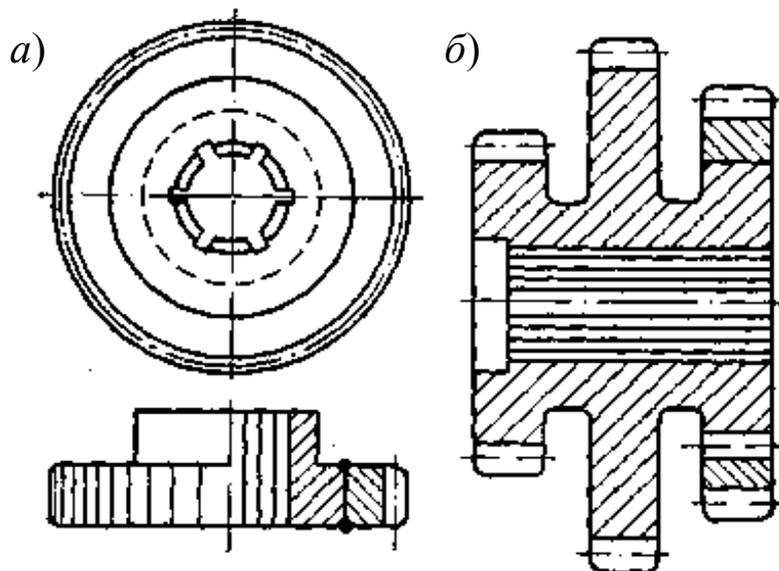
Восстановление зубчатых колес при помощи новых венцов: *a* – крепление зубчатого колеса на ободке колеса; *b* – то же на блоке зубчатых колес
